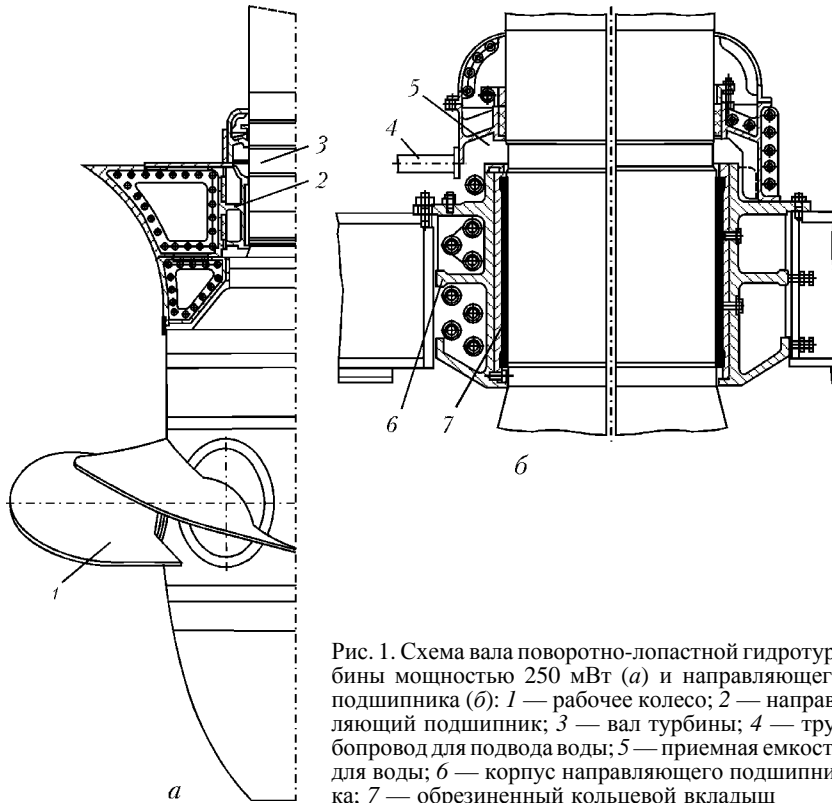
Схема вала поворотной-лопастной гидротурбины мощностью 250 мВт (а) и направляющего подшипника (б): 1 — рабочее колесо; 2 — направляющий подшипник; 3 — вал турбины; 4 — трубопровод для подвода воды; 5 — приемная емкость для воды; 6 — корпус направляющего подшипника; 7 — обрезиненный кольцевой вкладыш
